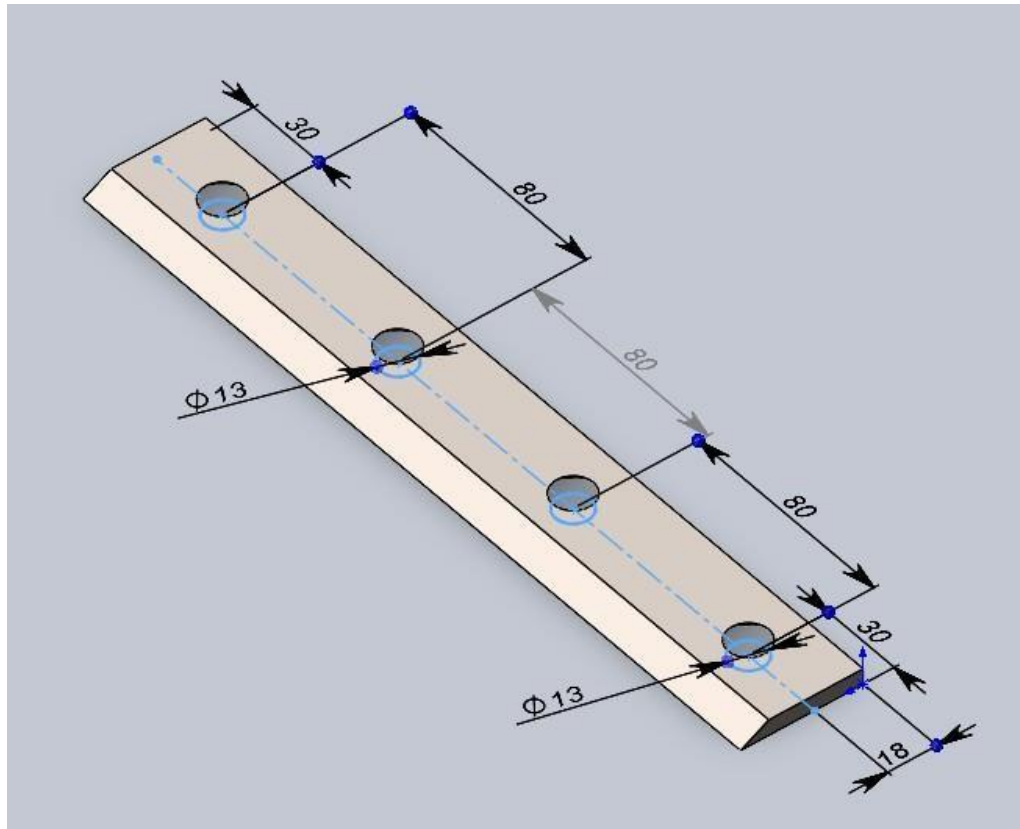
Загальний вигляд ножа подрібнювача
